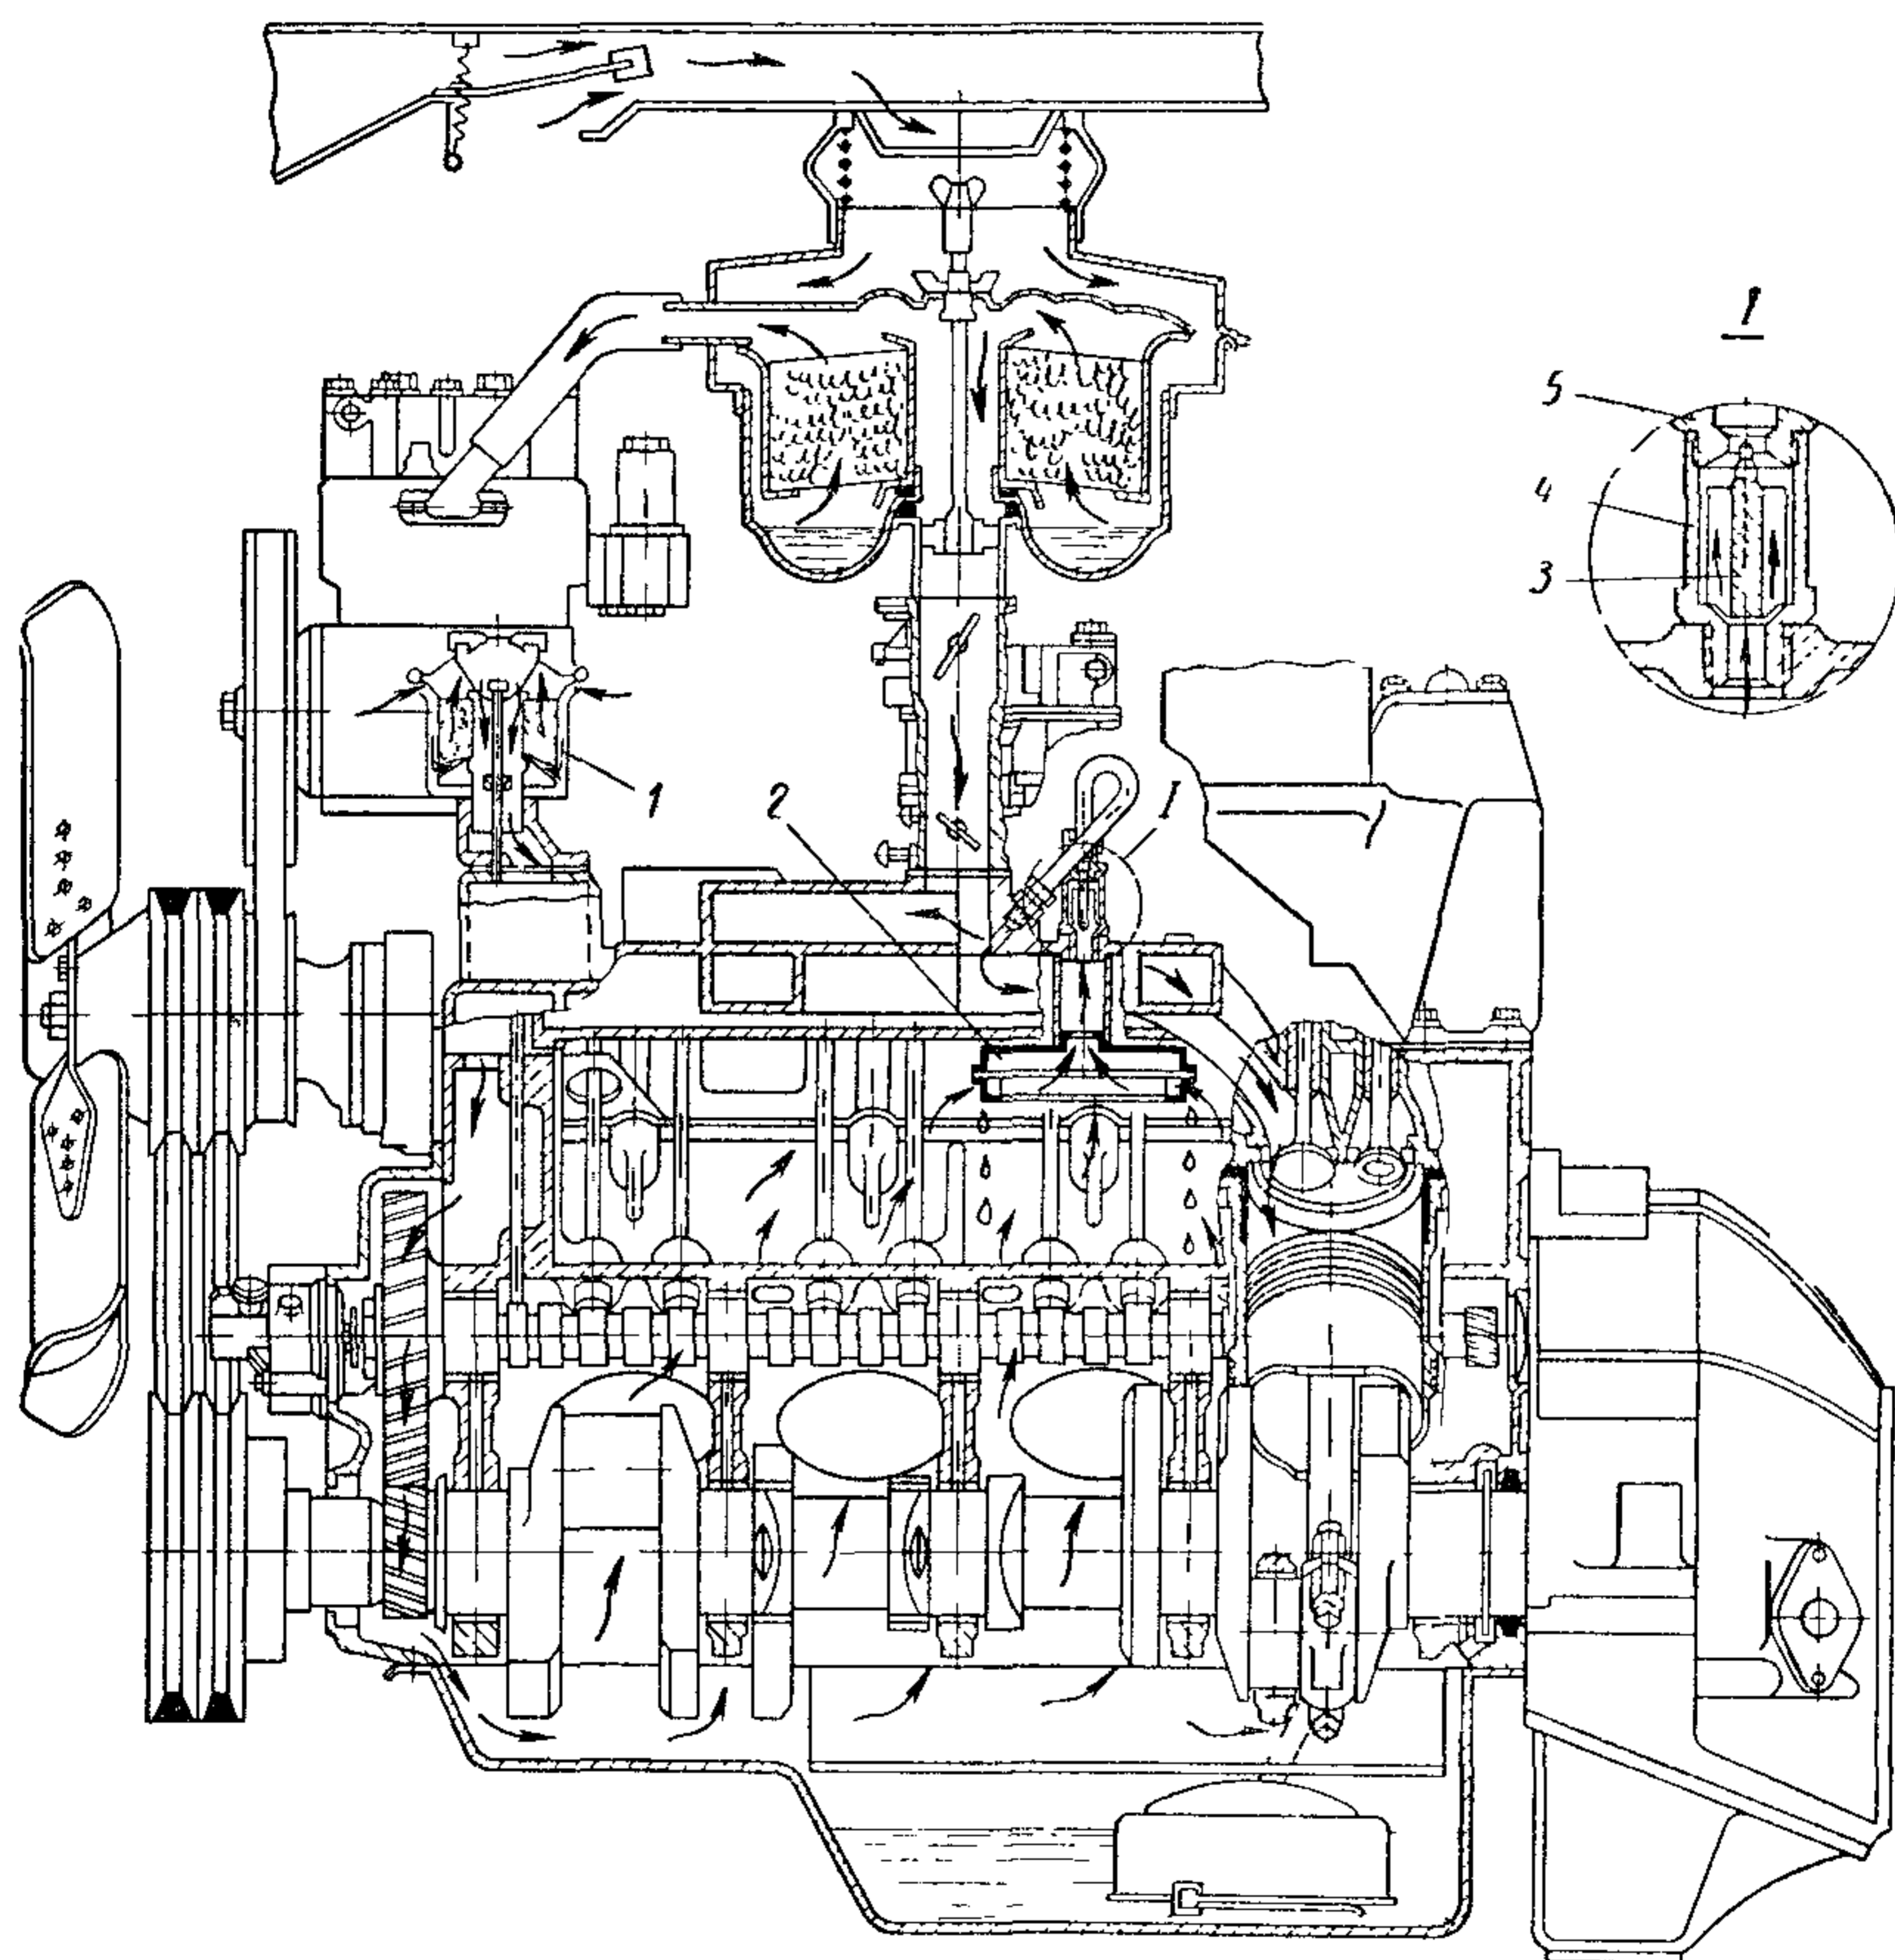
Схема вентиляции картера двигателя ЗИЛ-130 и питания его воздухом:
